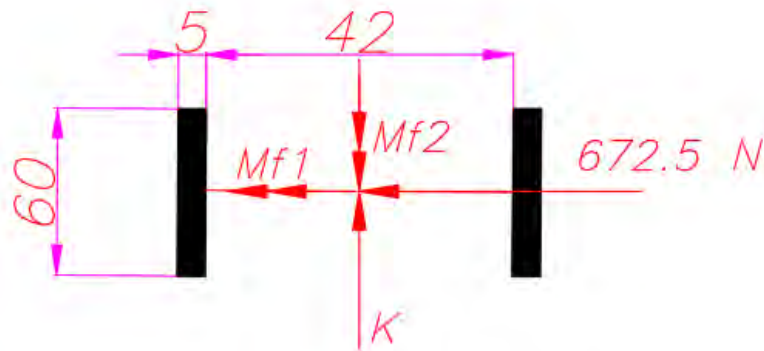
Fuerza de corte sobre garganta de soldadura – Escenario 2.
